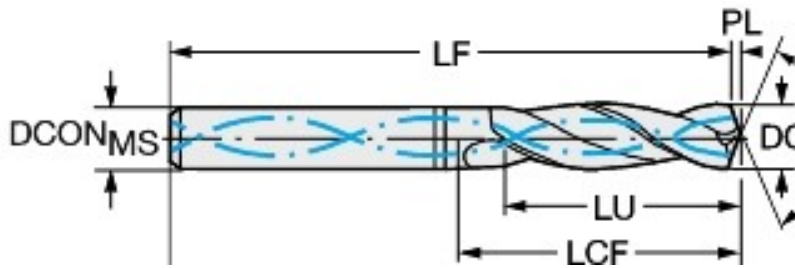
Сверло Coro Drill 860 860.1-0500-015A1-HM N10F
